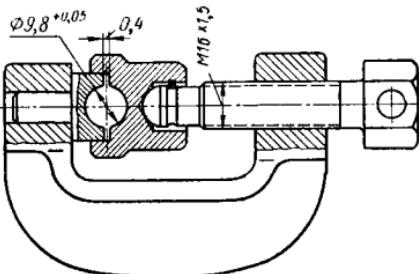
Приспособление для обжатия пластмассовых топливопроводов слива топлива из головок цилиндров
